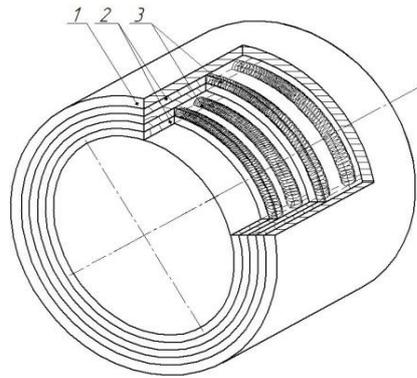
Схема вкладыша подшипника скольжения с металлической фазой в виде пружины: 1-опорная втулка; 2- слои проклеенной древесины; 3 – пружина
